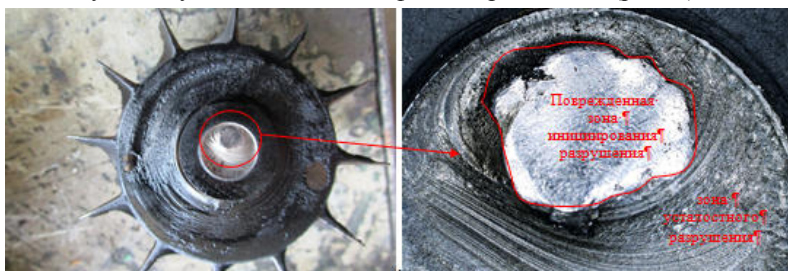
Излом вала, вследствие наличия дефекта сварного шва (непровара)
